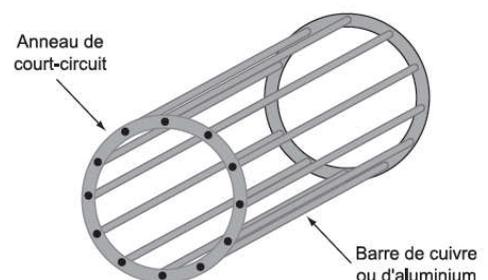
Rotor à cage d'écureuil d'un moteur asynchrone.
